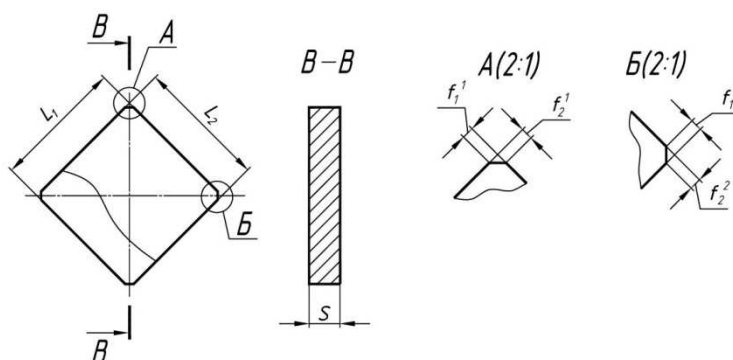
Эскиз резца из металлокерамической пластины после заточки
